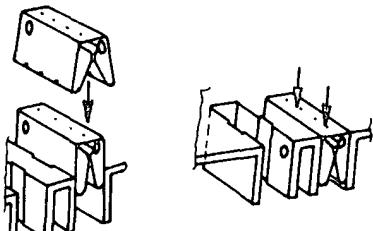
Základní modul stavebnice Kosmotronik má tvar kvádru. Zasunutím kolíčku tvaru X se dají spojovat kvádry vedle sebe. K zapojení se používají běžné součástky nebo moduly na deskách s plošnými spoji s drátovými vývody. Všimněte si jednoduchého provedení tlačítka vpředu vlevo. Obrázek je na třetí straně obálky
